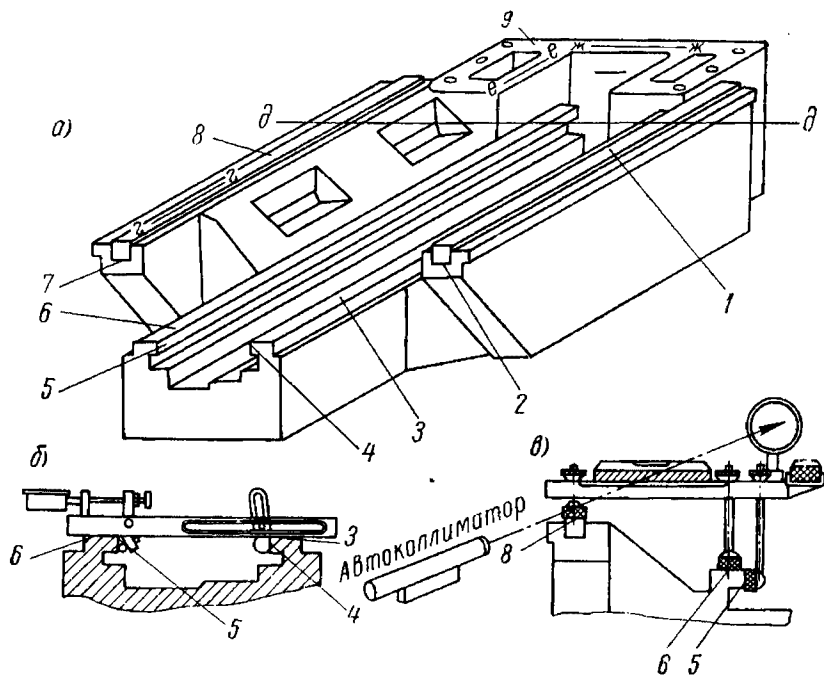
Станина станка 2450: а — общий вид; б и в — схемы проверки точности направляющих
